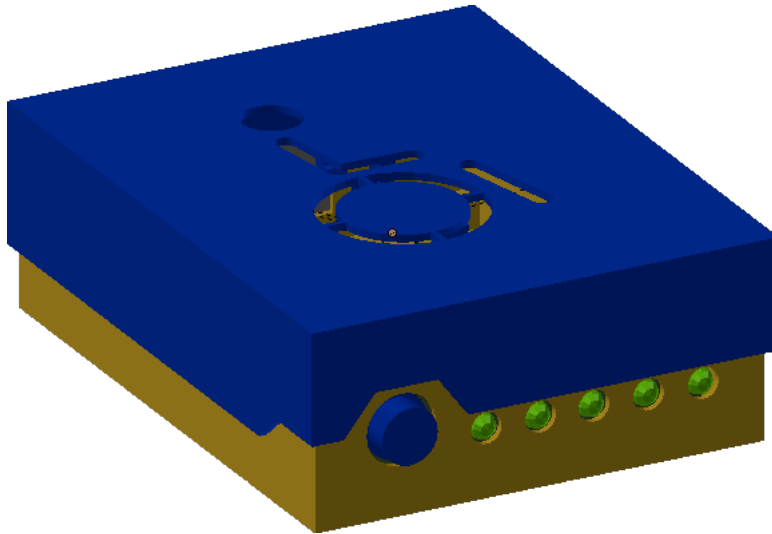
3D-Ansicht des ersten Gehäuse-Prototypen
